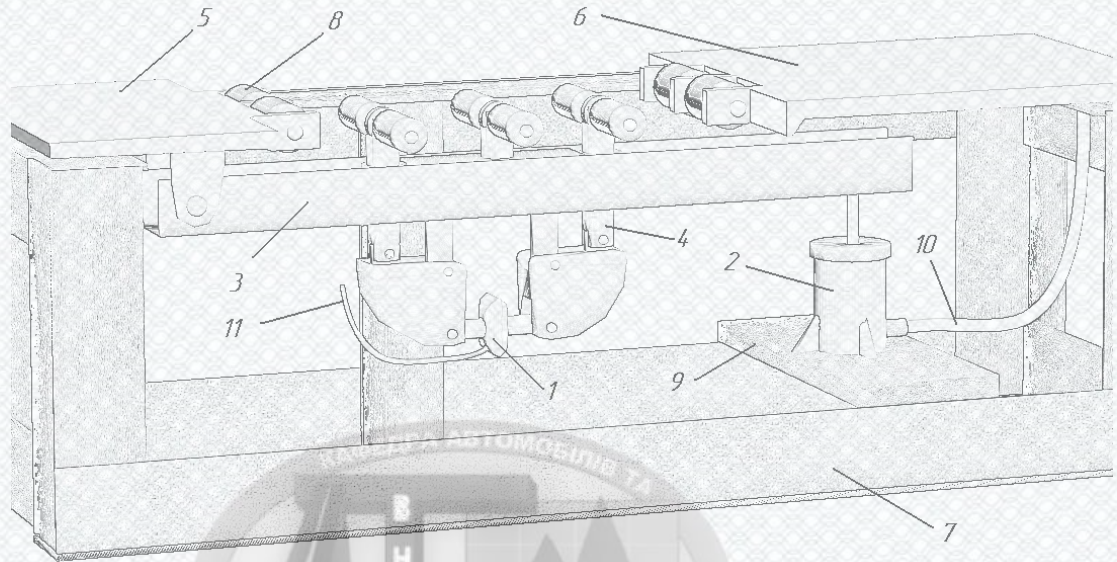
Загальний вигляд станду для контролю стану шин
